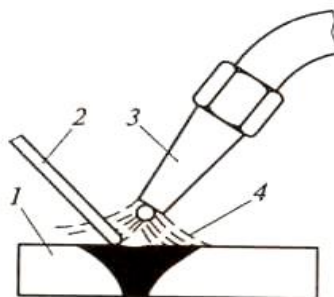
Схема газовой сварки: 1 – заготовки; 2 – присадочный прутки; 3 – сварочная горелка; 4 – сварочное пламя
